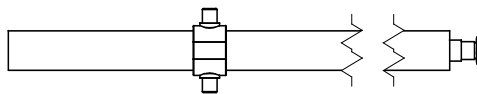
Konstrukce a součásti (na obrázku je typ ADS 120)
